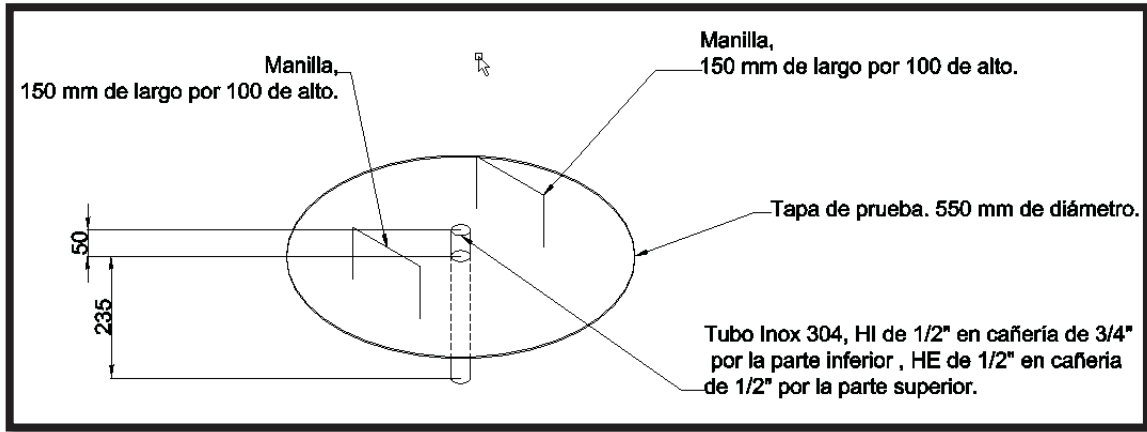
Diseño entregado en taller de soldadura para la construcción de la tapa de prueba. Las cotas que no se especifican y líneas de centro se omitieron para facilitar el entendimiento del diagrama por parte de los soldadores.
